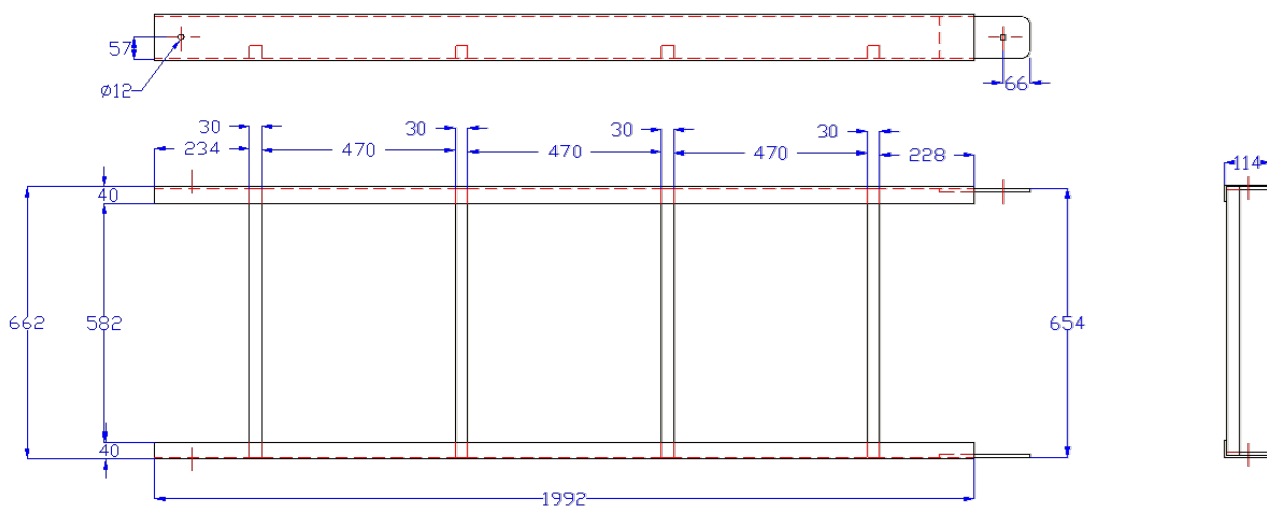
ELEMENTO PROLUNGA DA 2 METRI
